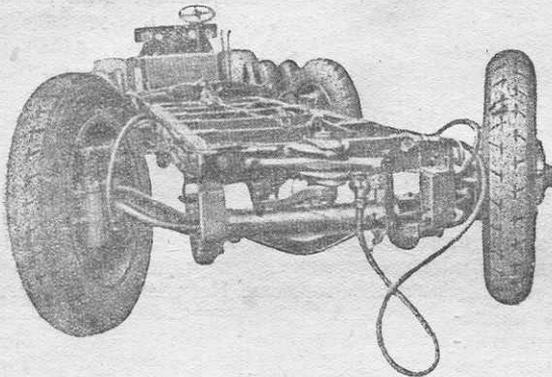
Шасси прицепа с поворотными осями. Шасси оборудована пневматическими тормозами.
